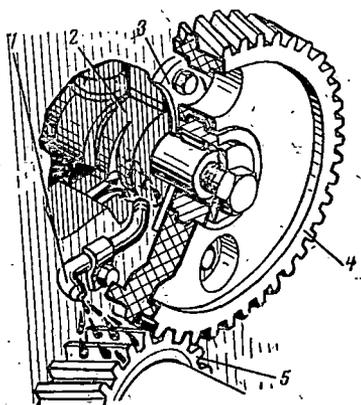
Схема смазки распределительных шестерен двигателя ГАЗ-51:
